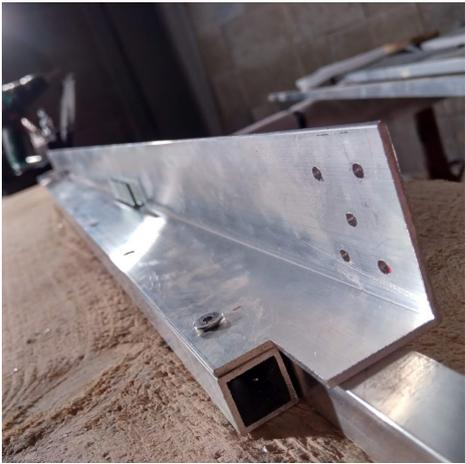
Winkel für Schwelle mit Aufstufdüchtung
